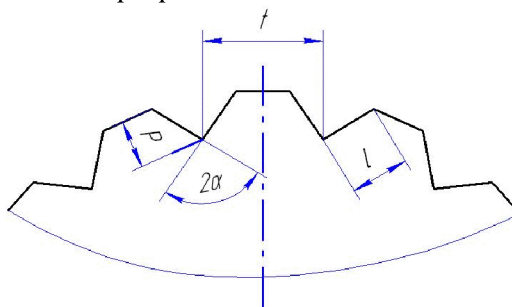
Профиль рифлений на боковой поверхности рабочей части пробивного пуансона
